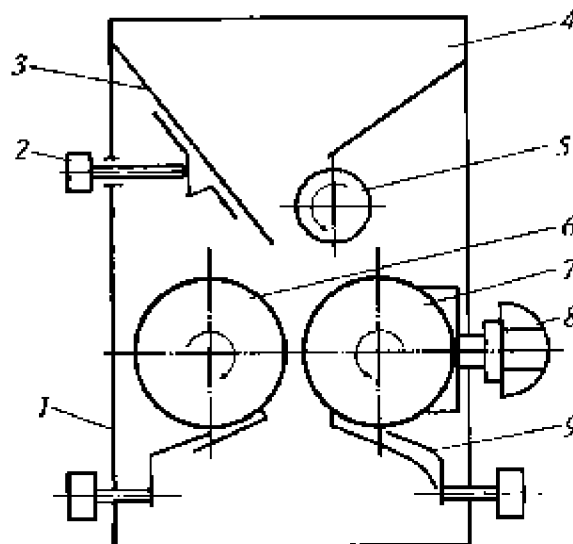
Вальцьовий механізм МДП-II-1: 1 – корпус; 2 – гвинт; 3 – шибер; 4 – бункер завантажувальний; 5 – валок живильний; 6, 7 – валки розмелювальні; 8 – рукоятка; 9 – скребок
